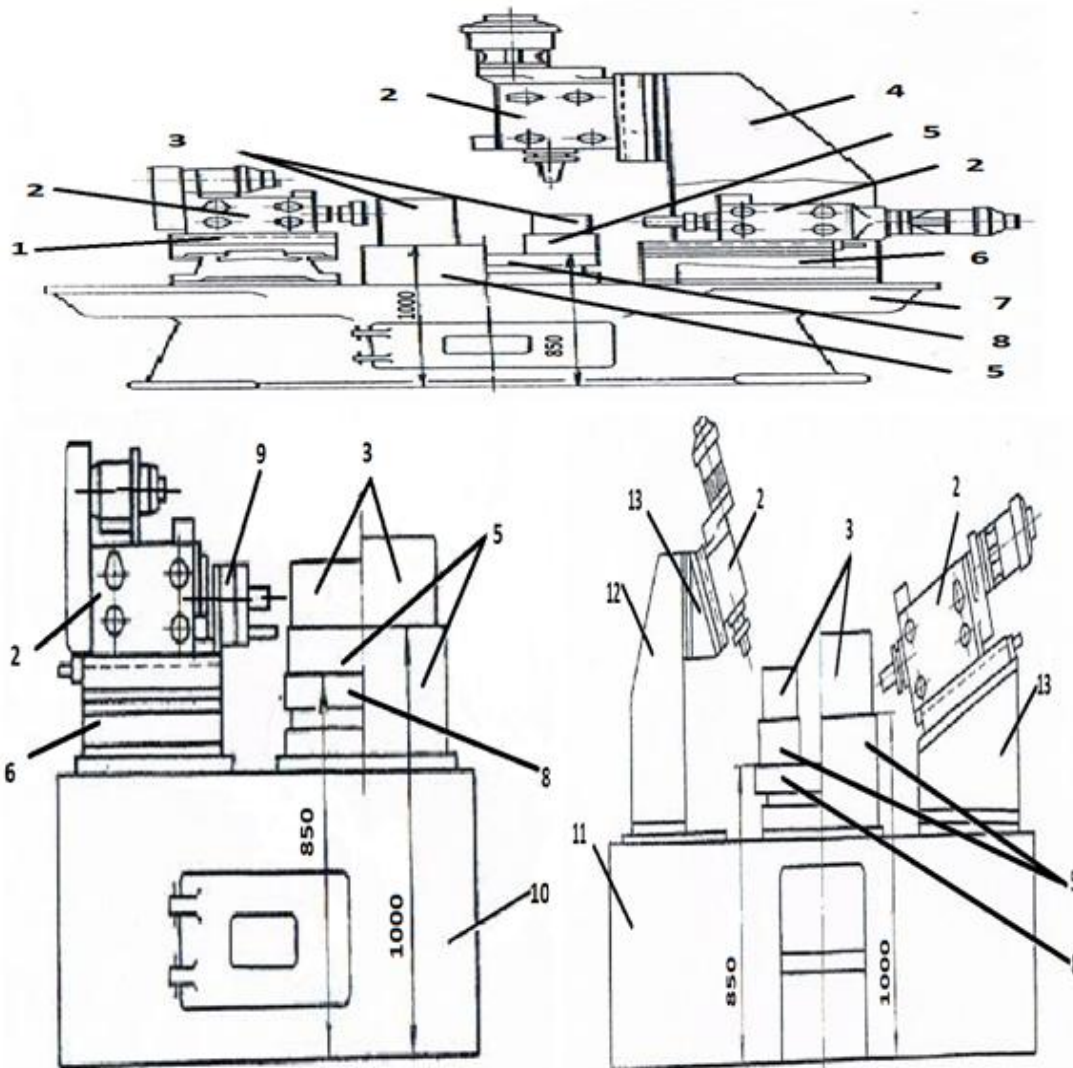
Ensembles principaux et certaines dimensions des petites machines à unités autonomes : 1.Table d'usinage; 2.Tête d'usinage; 3.Pièce à usiner; 4.Bâti vertical du type à arcade; 5.Dispositif; 6.Plaque intercalaire droite; 7.Bâti circulaire; 8.Plateau diviseur; 9.Adaptation multibroche; 10.Bâti unilatéral; 11.Bâti bilatéral; 12.Montant; 13.Plaque-équerre intercalaire
